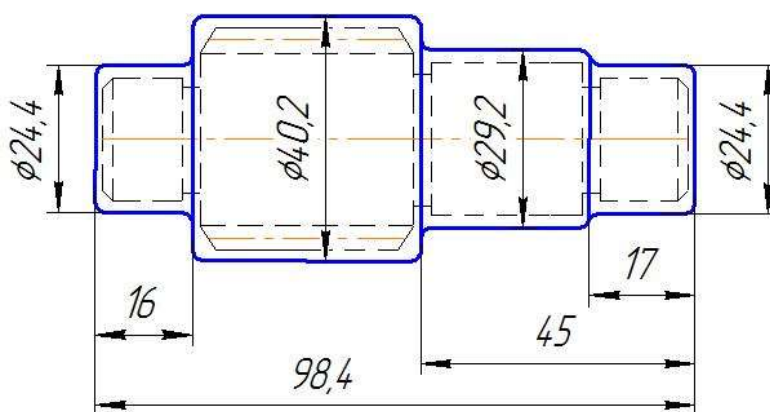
Заготовка отримана штампуванням на КГШП
